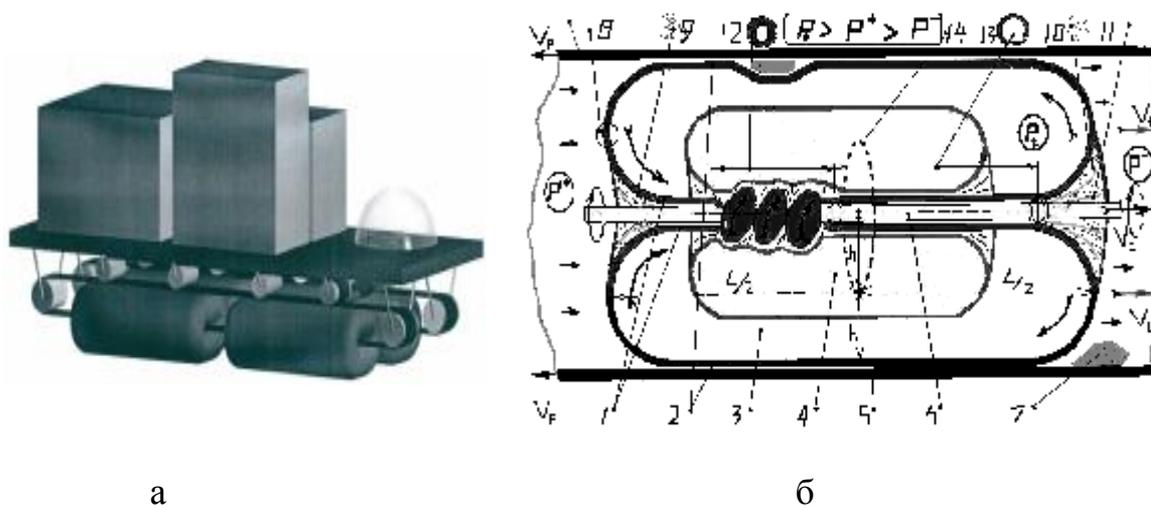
Мягкий пневматический тороидальный движитель транспортного средства: а – общий вид макета транспортного средства; б – комплексный эластичный (тороидальный) механизм
